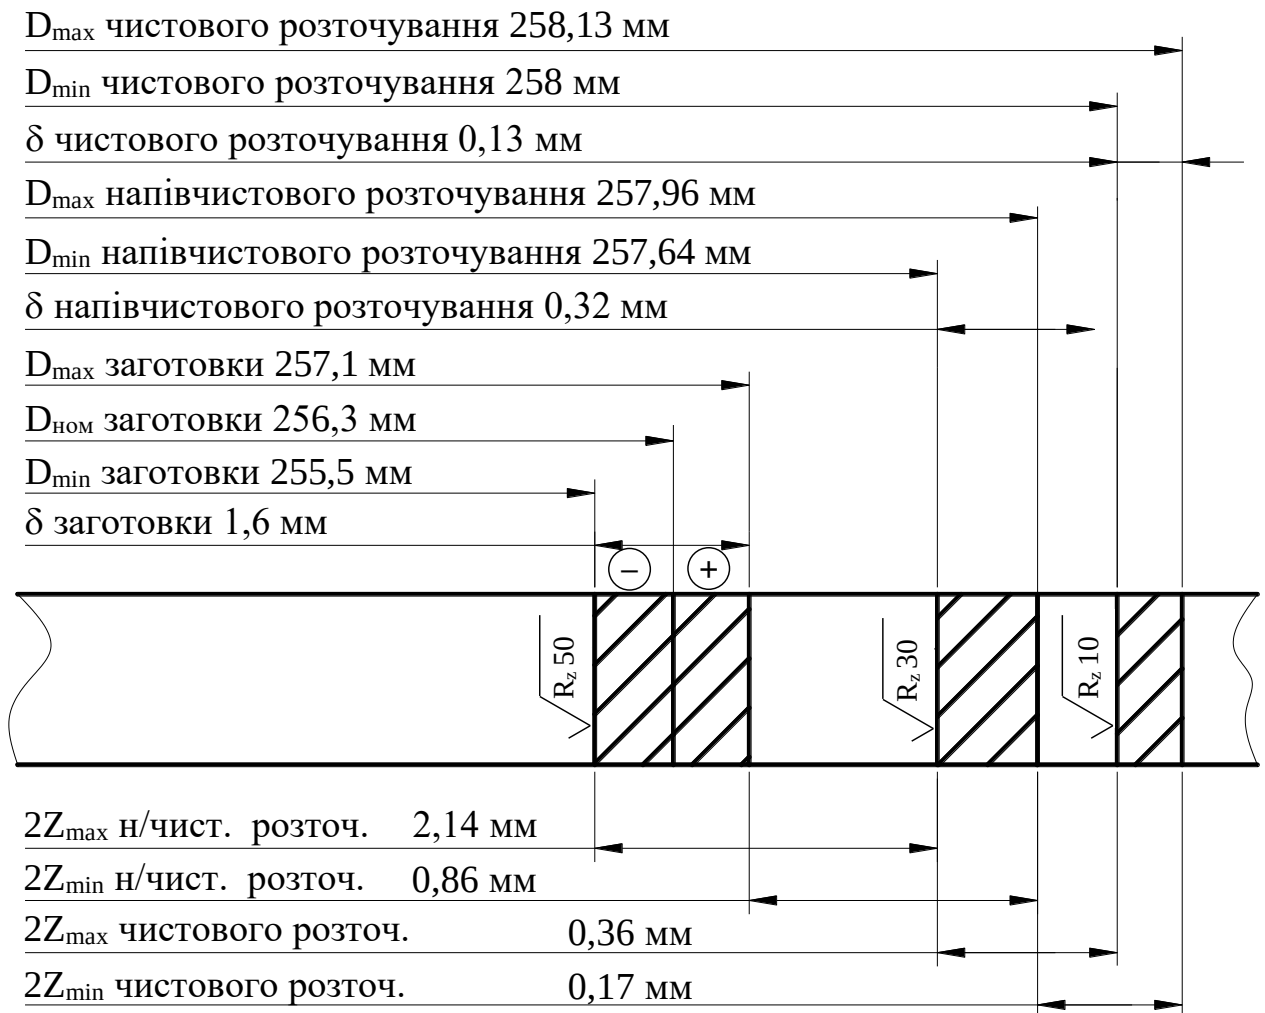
Схема розташування припусків та допусків при обробленні поверхні $\varnothing 258^{+0,130}$
